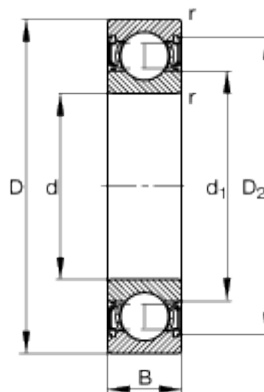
Rodamiento Rígido de Bola 6205(Corona)
